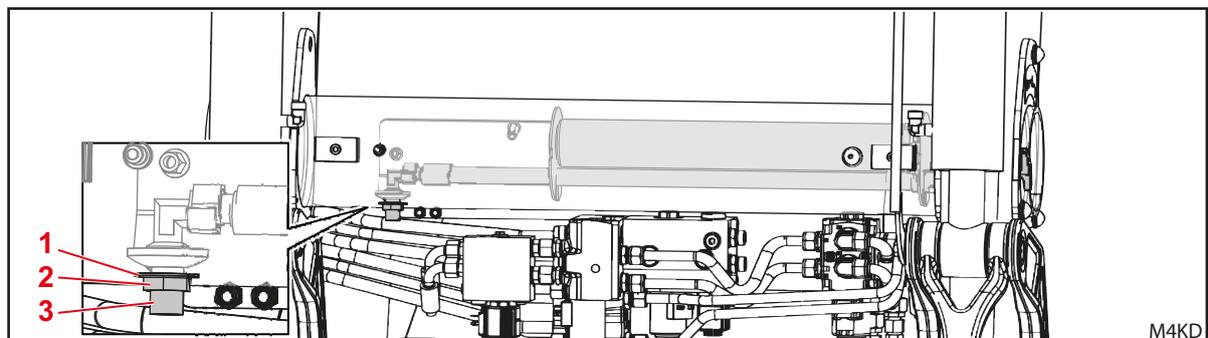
Comfort-Drive fissato nel tubo trasversale
